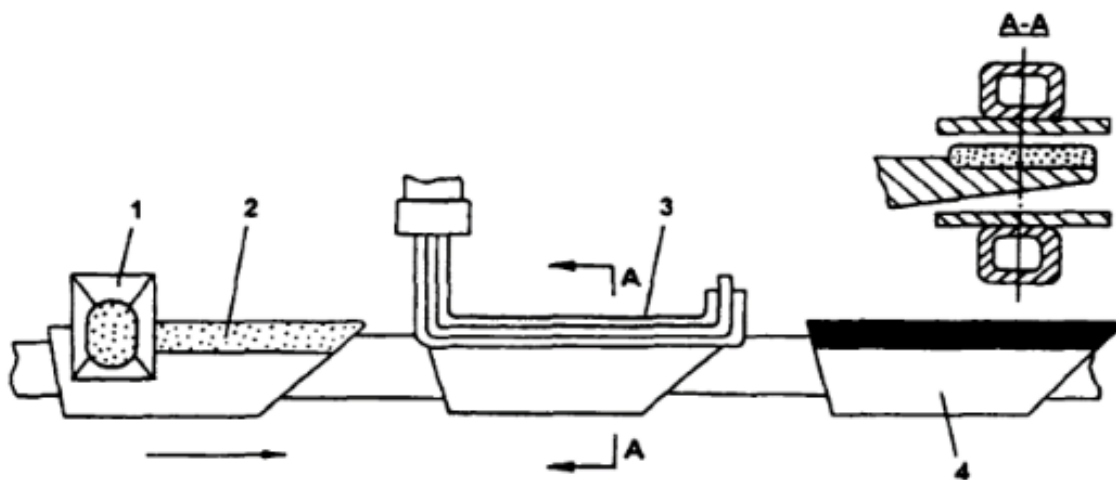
Схема процесу одночасного наплавлення леза лемеха
